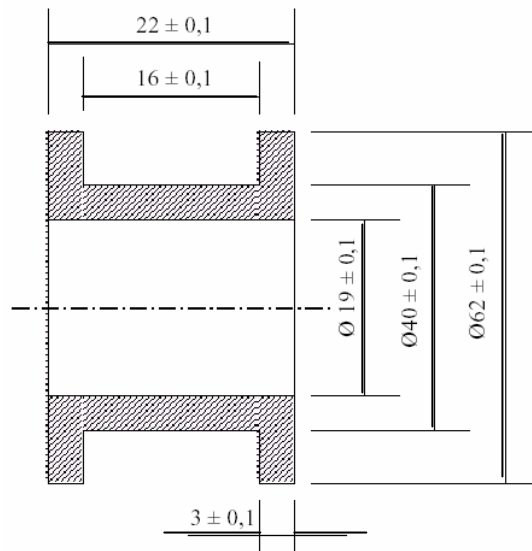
Vista com corte do corpo de prova com as dimensões definitivas
